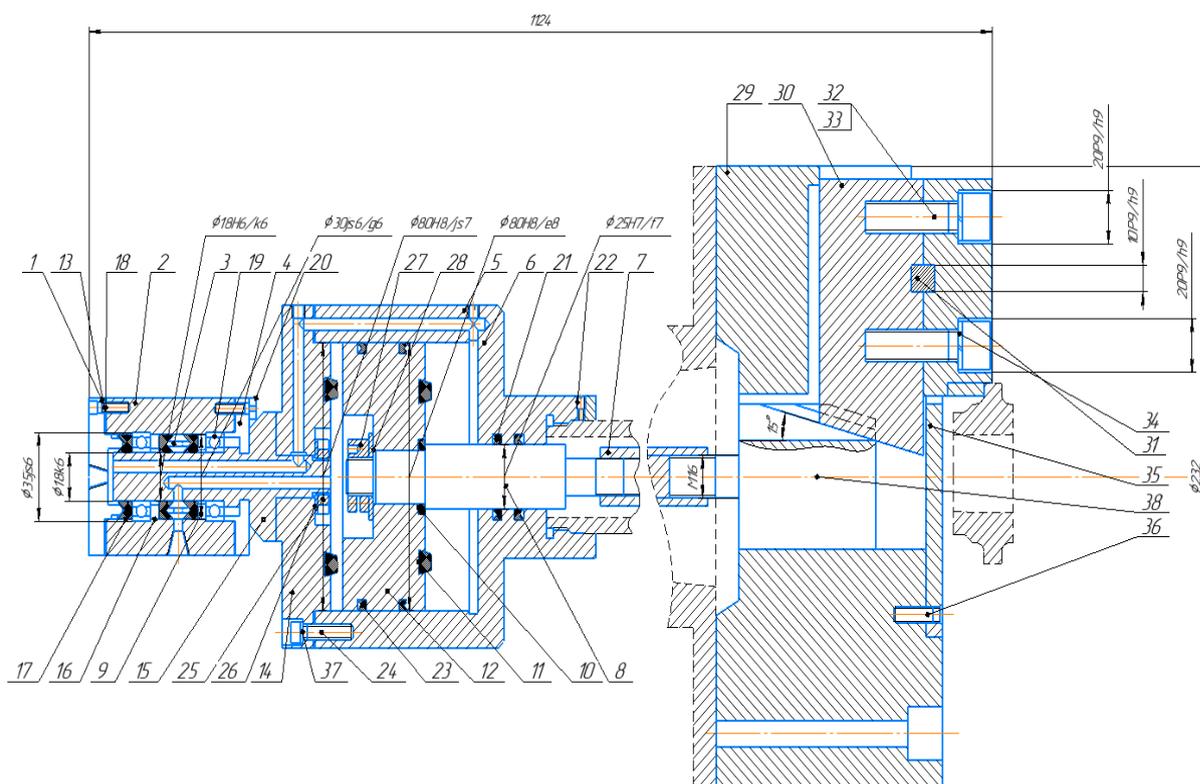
Общий вид трёхкулачкового гидравлического патрона
